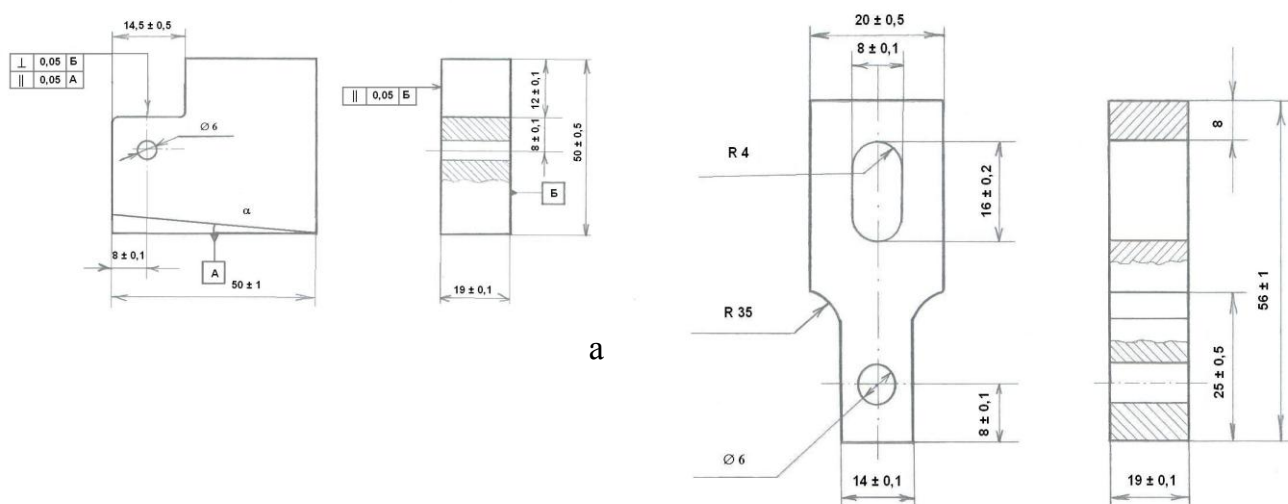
Образцы из УУКМ типа ТЕРМАР для физико-механических испытаний: (а) – модельный образец на сжатие, (б) – модельный образец на растяжение.
